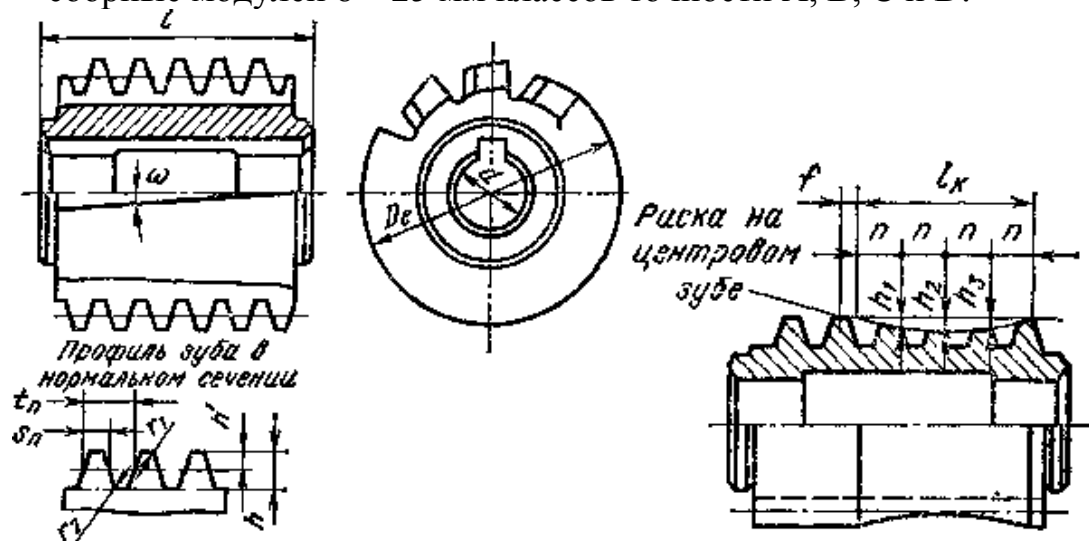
Схема черновой червячной фрезы с переменной высотой зуба.
